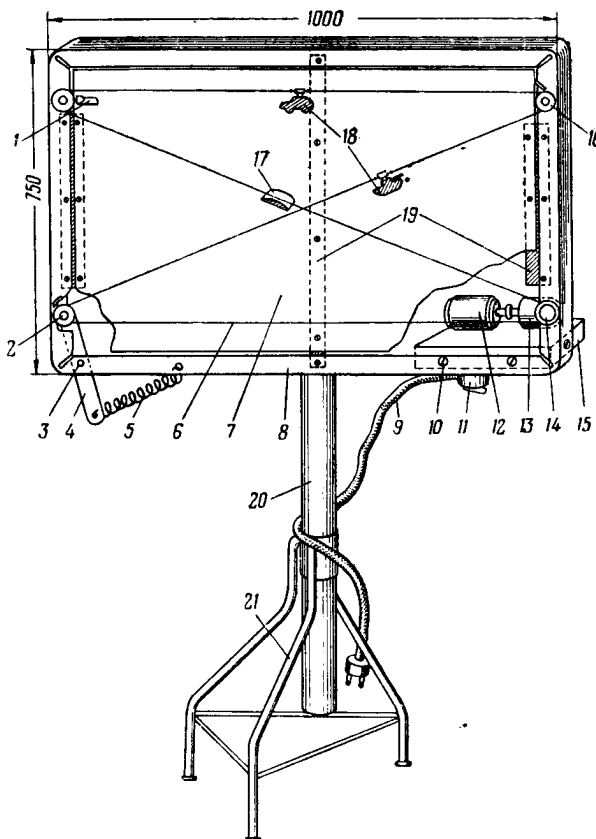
Прибор для тренировки в стрельбе по движущимся целям: 1 — отсекатели целей; 2 — ось с роликом; 3 — ось стойки; 4 — стойка; 5 — оттяжная пружина; 6 — привод; 7 — экран; 8 — рамка; 9 — провод; 10 — шуруп; 11 — выключатель; 12 — электродвигатель; 13 — редуктор; 14 — ведущий ролик; 15 — подставка; 16 — обратный ролик; 17 — брусок; 18 — цели; 19 — планки крепления экрана; 20 — труба; 21 — тренога.
